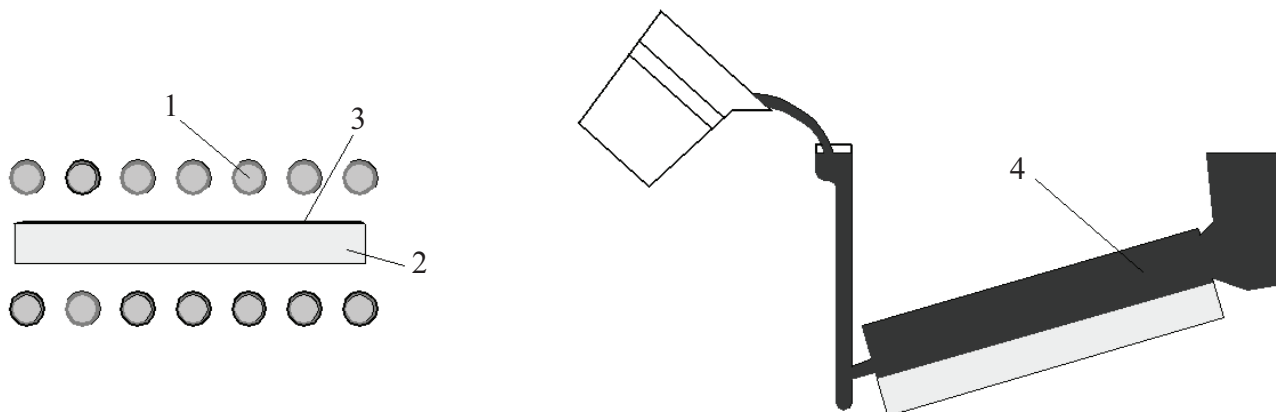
Схема технологического процесса изготовления биметаллических отливок способом заливки жидкого металла на твердую заготовку: 1 – водоохлаждаемый индуктор; 2 – твердая стальная заготовка; 3 – защитное покрытие; 4 – износостойкий чугун
